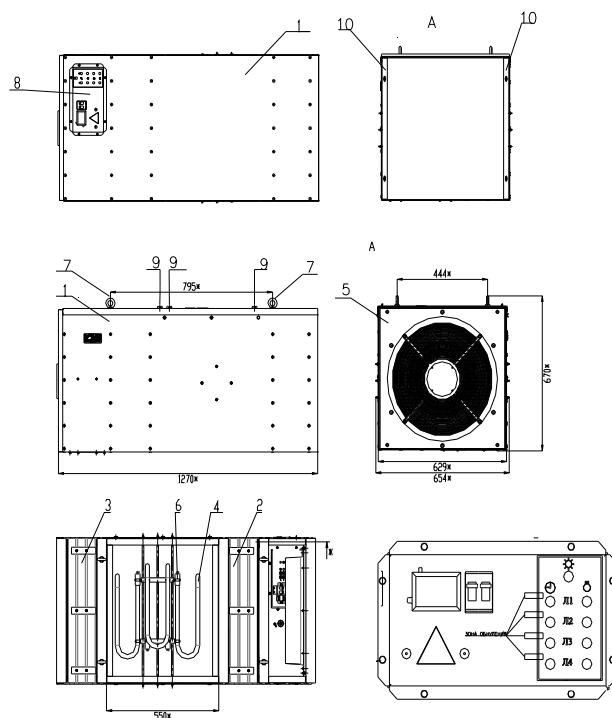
Общий вид и габаритные размеры рециркулятора АЭРОЛИТ-3000
